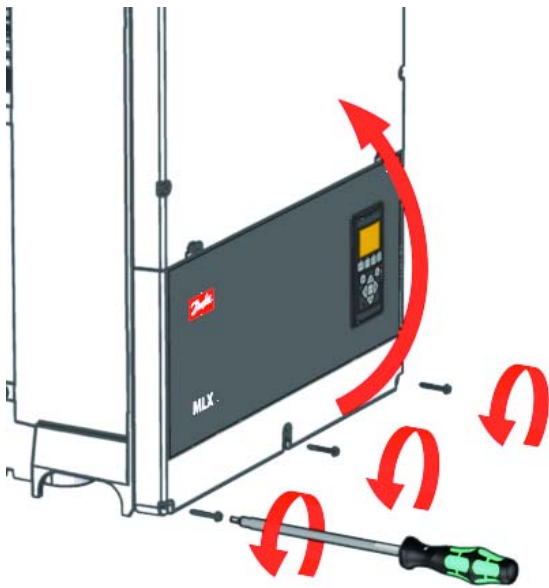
Aflojelo los tornillos frontales y levante la cubierta
